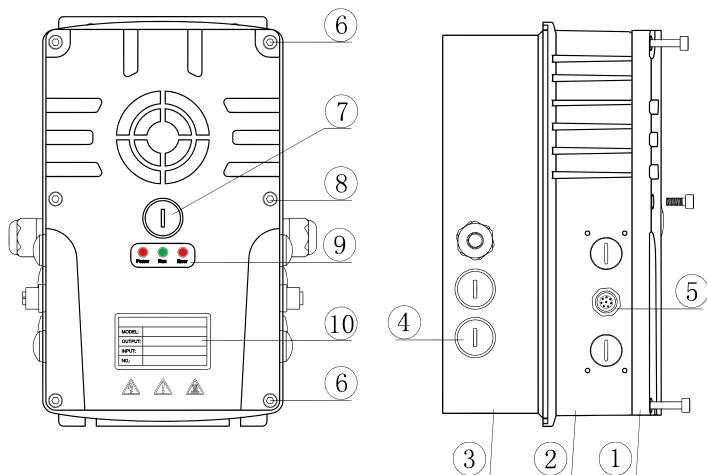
Устройство преобразователя частоты для монтажа на двигатель
